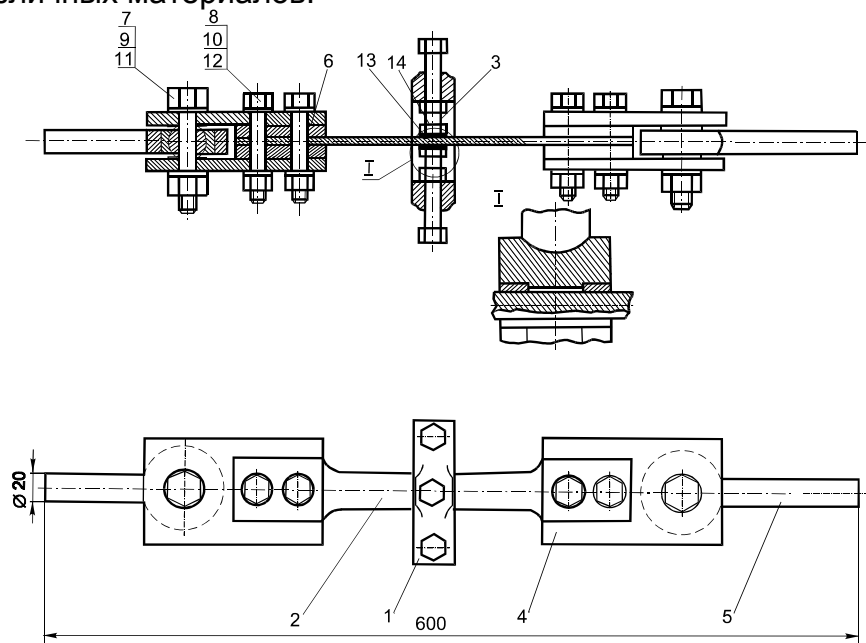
Образец и приспособление для исследования влияния величины контактных давлений и сочетания материалов в контактной паре на усталостную долговечность гладкой полосы в условиях фреттинг-коррозии: 1 – скоба; 2 – образец; 3 – прижимной болт; 4 – пластина; 5 – проушина – захват; 6 – прокладка; 7 – 12 – крепежные детали; 13 – шайба; 14 – прижим
